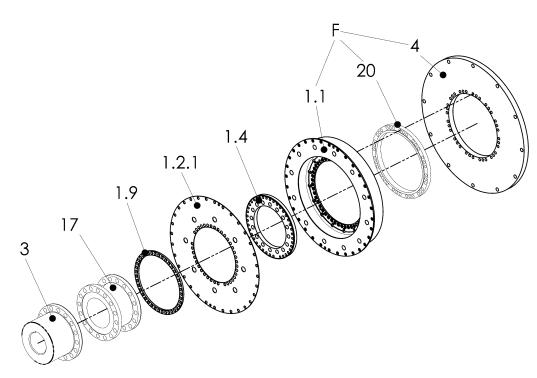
Beispiel: 020G-00050...00090-F.10
